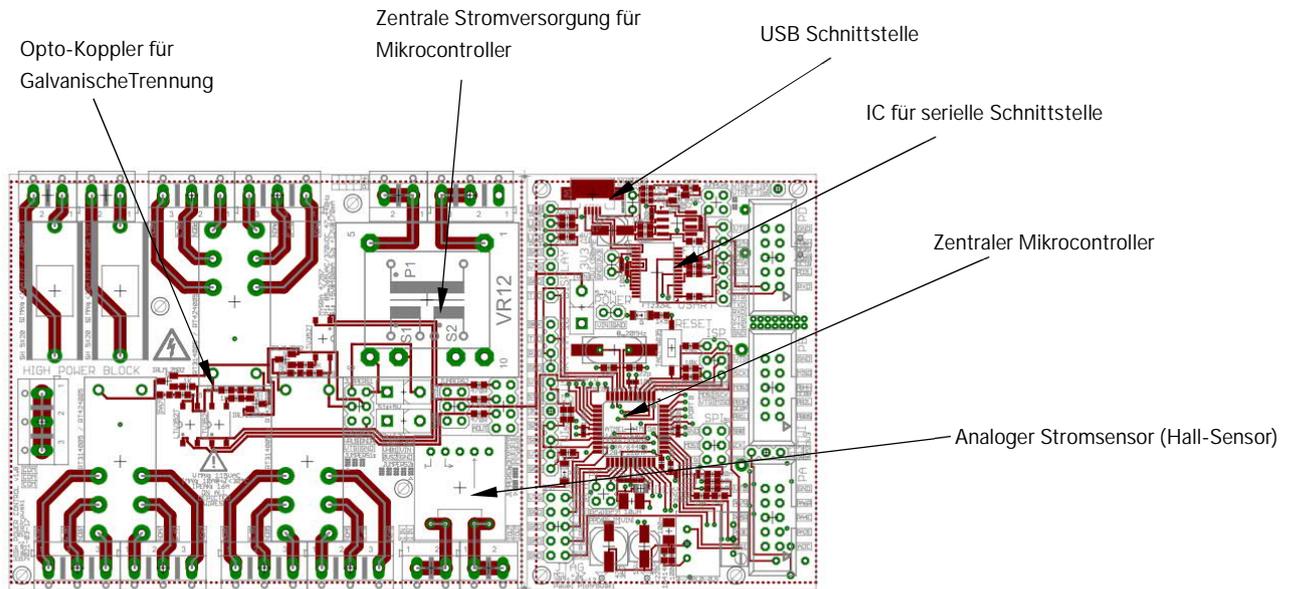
Platine des Mess-Sendemoduls: Draufsicht
